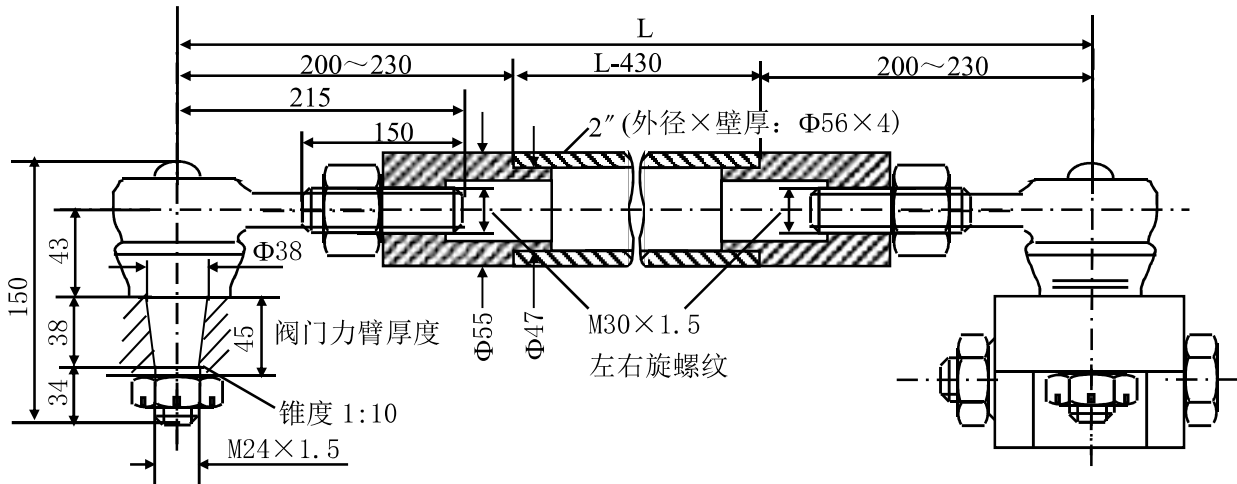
RHA6000/8000 杠杆连接器外形尺寸图
